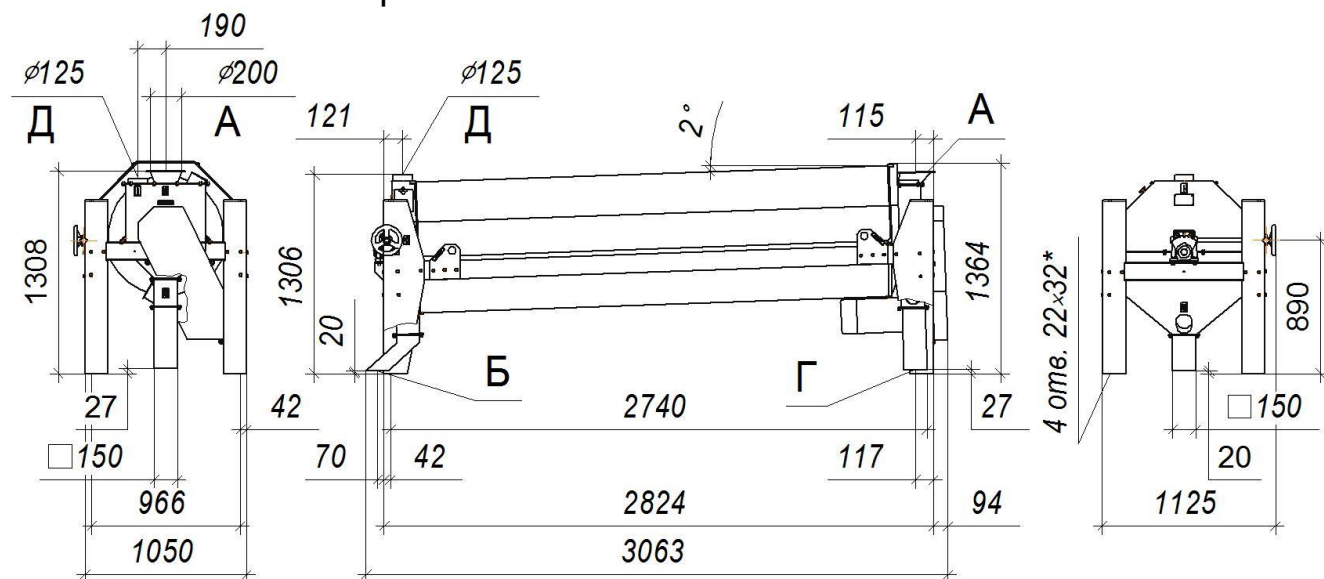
Установочные и присоединительные размеры триеров цилиндрических ТК-800-8; ТК-800-8Е; ТО-800-8 и ТО-800-8Е:
